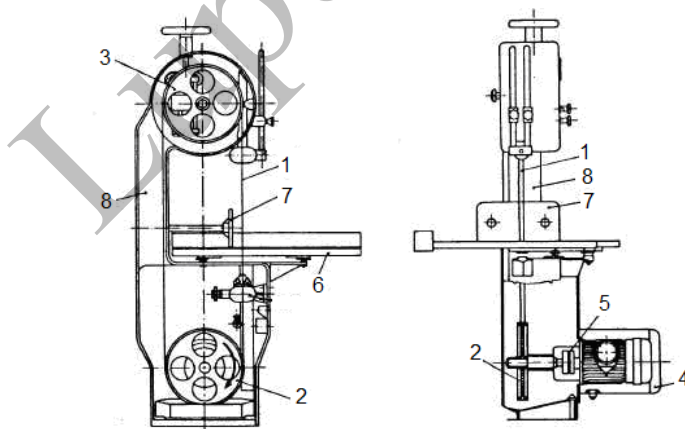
Fierăstrău lamelar staționar: 1- pânză lamelară; 2- roată acționare; 3- roată de întindere; 4- motor electric; 5- cuplaj elastic; 6- platformă cu role; 7- limitator; 8- corp fierăstrău
